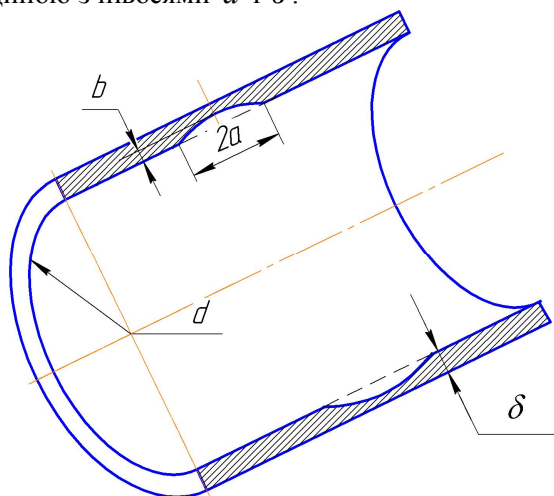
Типове розташування тріщини на внутрішній поверхні труби
